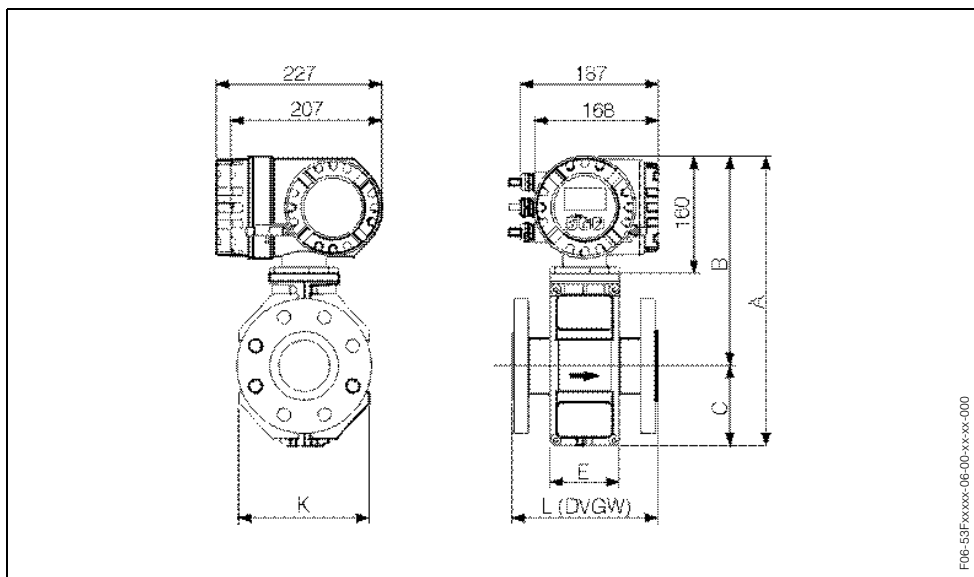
Dimensiones del Promag W / DN ≤ 300 (versión compacta)
